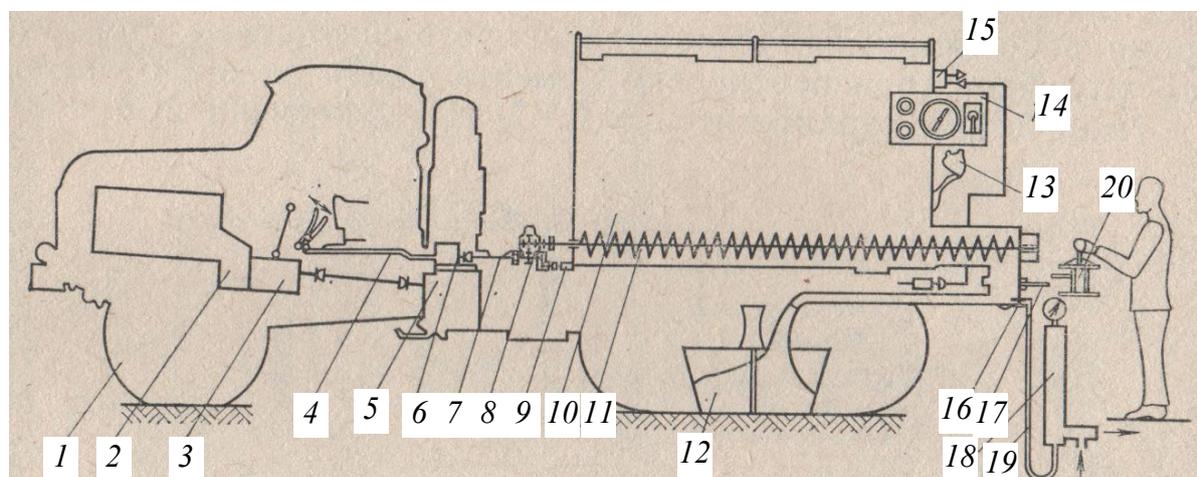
Схема управления цементосмесительной машиной СМ4М: 1 – шасси автомобиля ЗИЛ131А; 2 – двигатель автомобиля; 3 – коробка передач; 4 – управление коробкой отбора мощности; 5 – шпрота раздаточная; 6 – коробка отбора мощности; 7 – вал карданный; 8 – редуктор; 9 – датчик тахометра; 10 – бункер; 11 – шнек; 12 – бачок цементирующего агрегата; 13 – фара поворотная с выключателем; 14 – щиток приборов с тахометром, включением зажигания а двумя контрольными лампами; 15 – вибратор пневматический С80; 16 – штуцер сменный; 17 – шибер приемной воронки; 18 – регулятор давления; 19 – труба обводная; 20 – рычаг дублирующего управления с педалью
